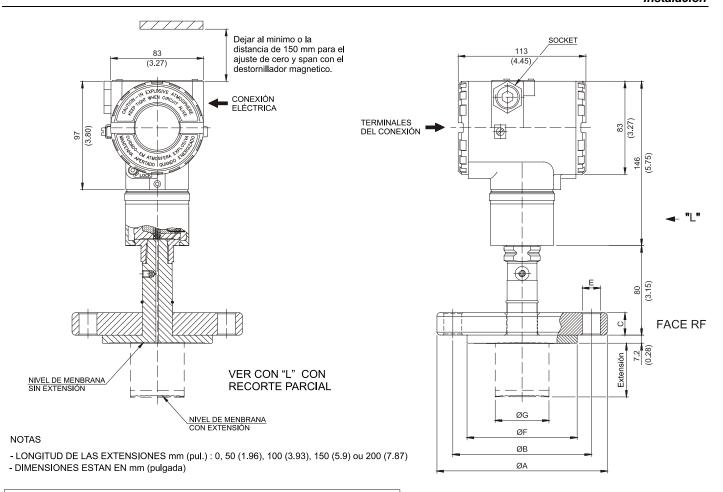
(b) – Diseño Dimensional de Montaje del LD291- Sanitario
